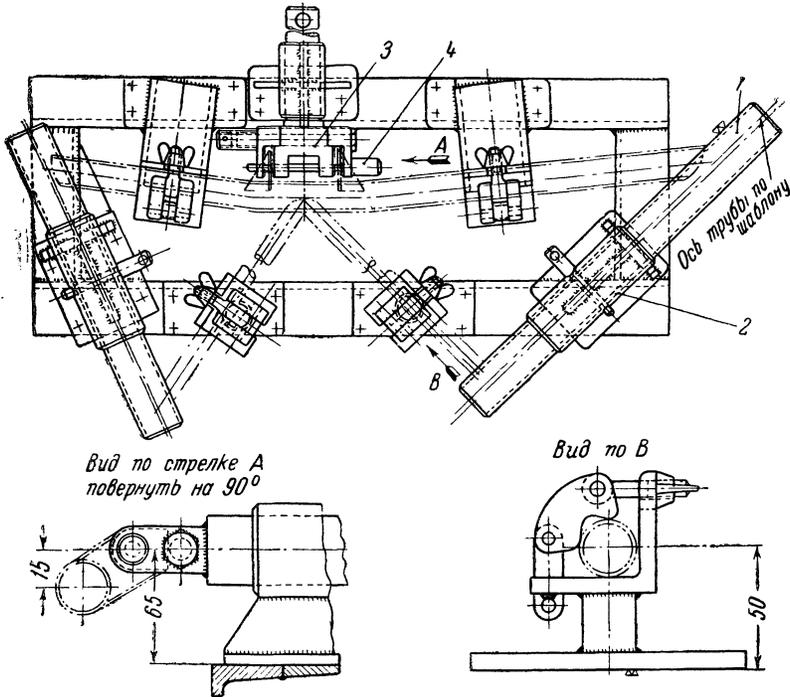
Приспособление для сборки и прихватки фермы костью.
